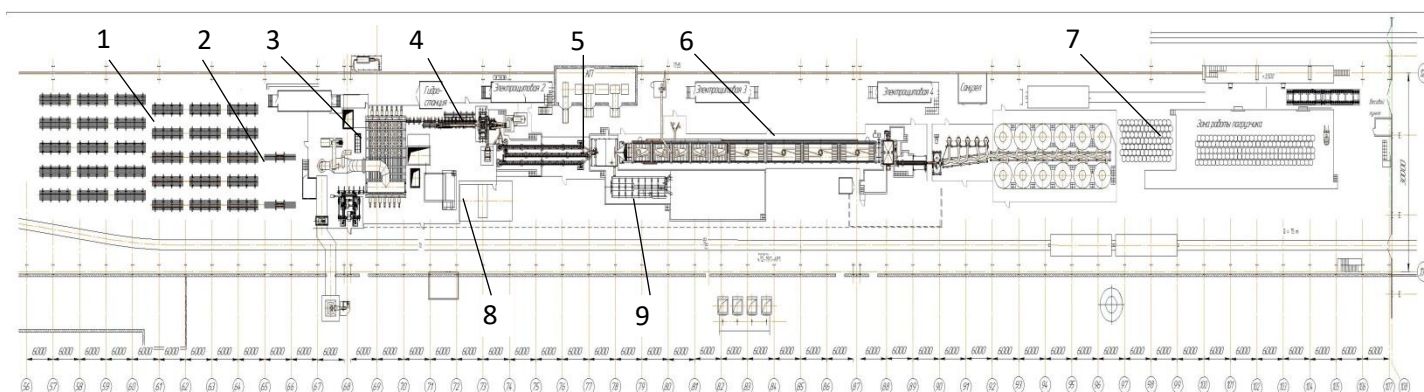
Схема расположения основного оборудования шаропрокатного комплекса
